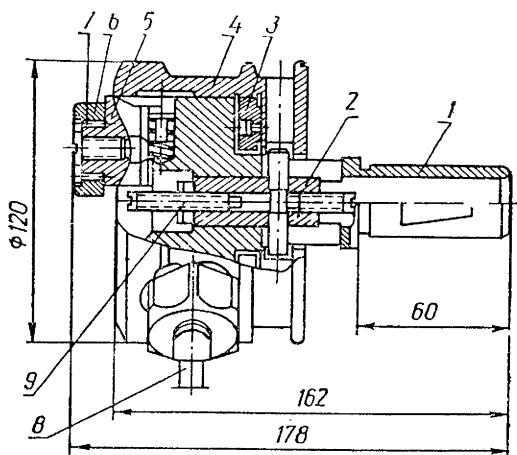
Самооткрывающаяся резьбонакатная головка.
